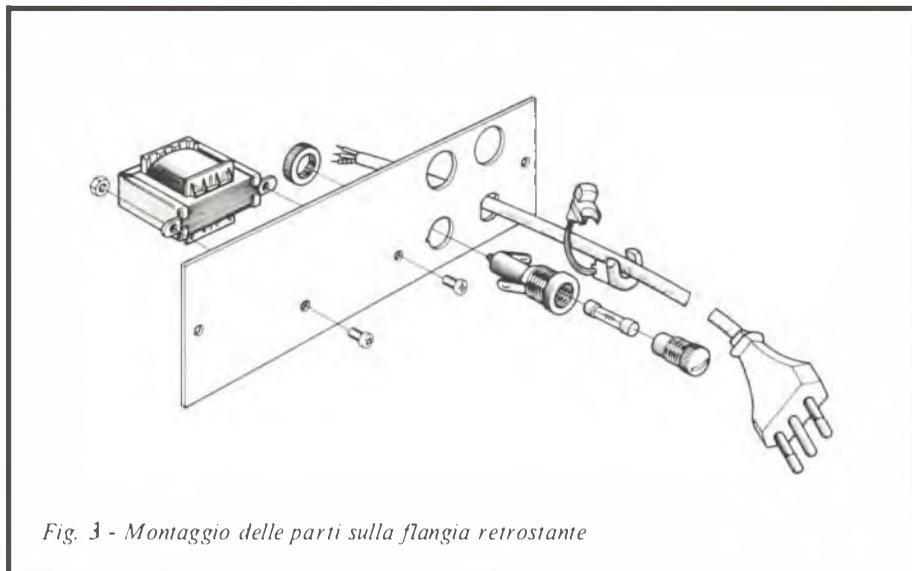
Montaggio delle parti sulla flangia retrostante
